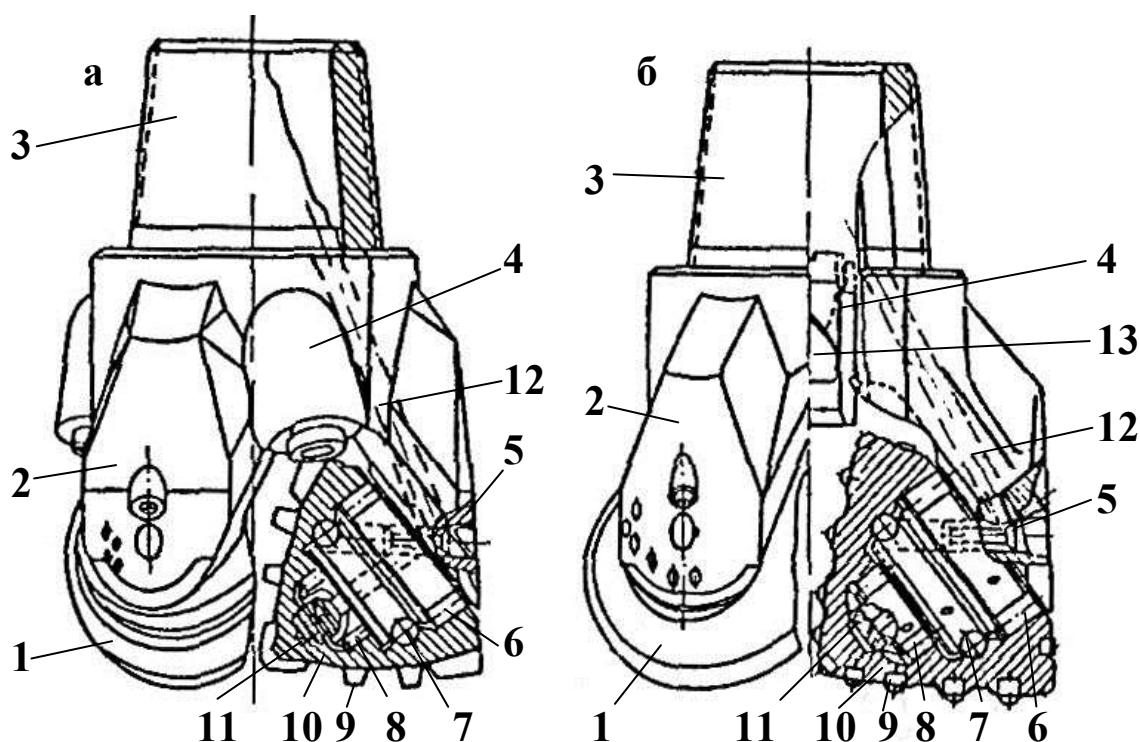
Конструктивные схемы трехшарошечных долот: а – зубчатого с фрезерованным вооружением шарошек и периферийной продувкой; б – штыревого с вооружением цилиндрическими элементами из твердого сплава и центральной продувкой
